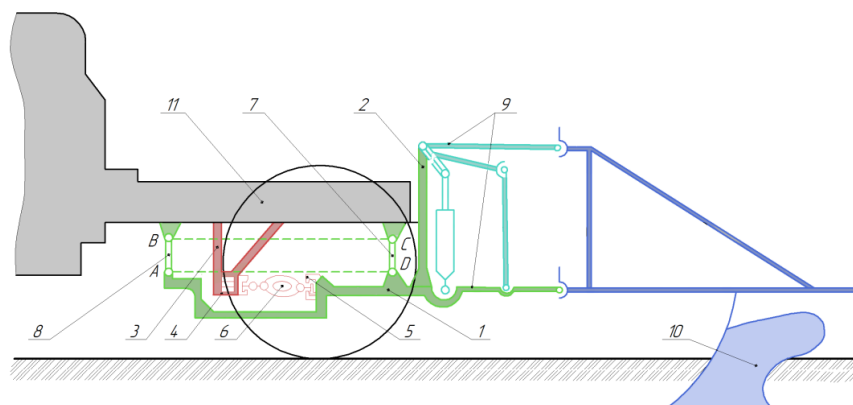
Кінематична схема пристрою для вимірювання тягового опору машини (для тракторів нетрадиційного компоновання з шарнірно-ламанною рамою): 1 – несуча рама; 2 – кронштейни циліндрів; 3 – тягово-зчіпний механізм; 4 – брус; 5 – замок; 6 – первинний вимірювальний перетворювач; 7 – задній
